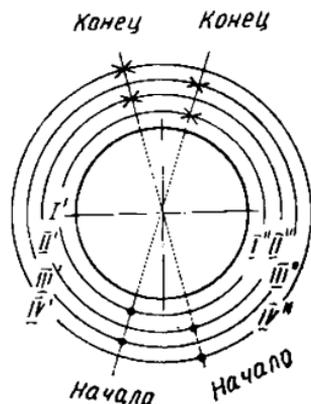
Схема наложения шва неповоротного стыка при ручной электродуговой сварке
